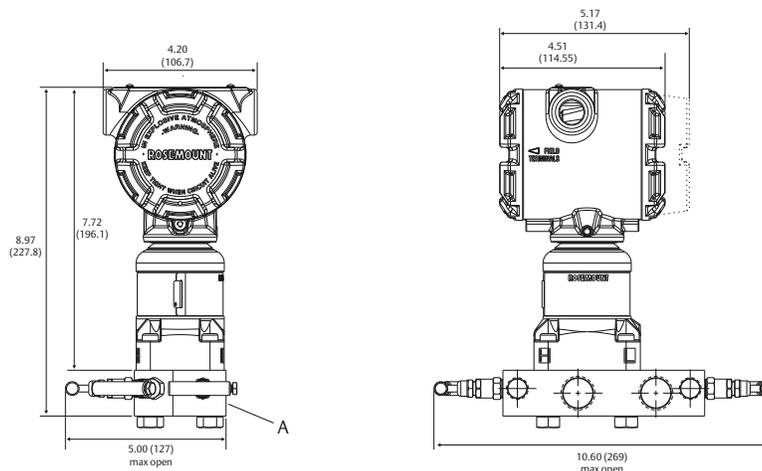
Копланарный клапанный блок модели 305 с тремя вентилями и боковым входом
